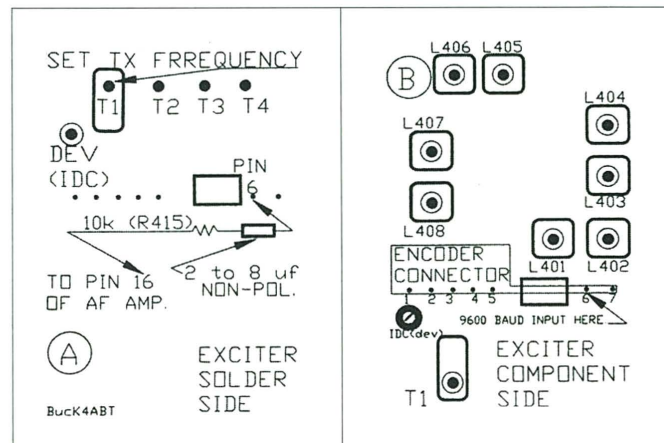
Lado de soldaduras del excitador (A) y lado de componentes (B).
